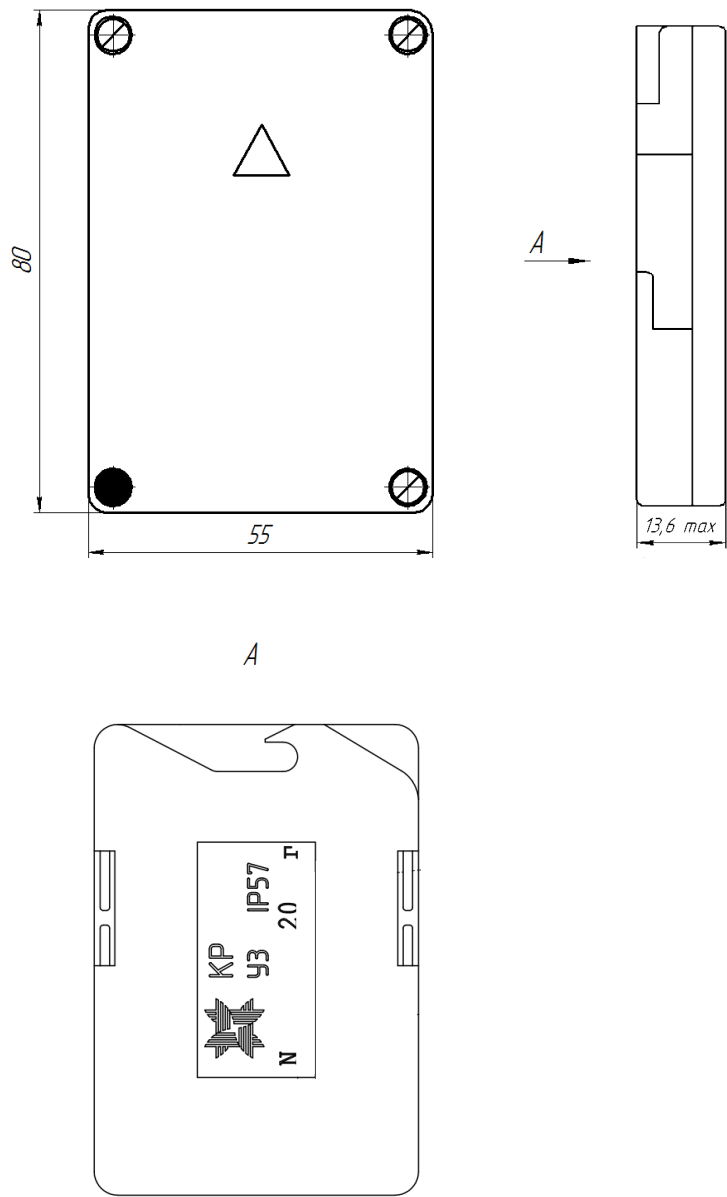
Внешний вид и габаритные размеры кассеты
